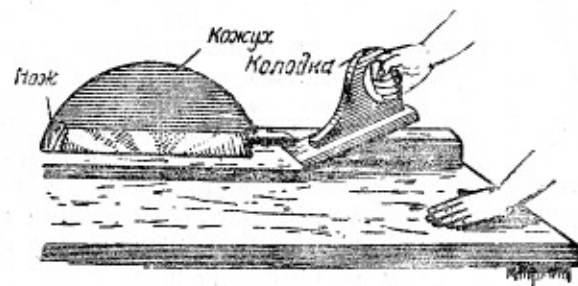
Расклинивающий нож, защитный кожух и предохранительная колодка
